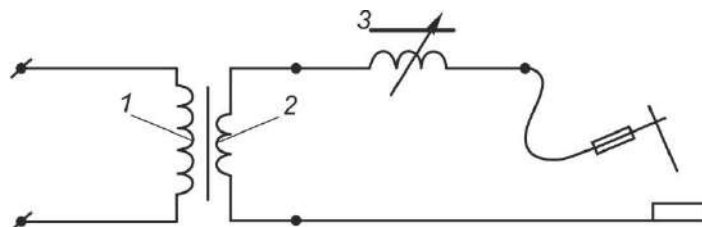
Схема включения сварочного трансформатора
